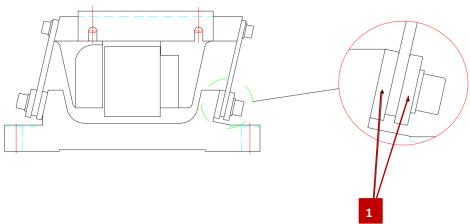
Ensemble de ressorts avec plaques de réglage (1)
